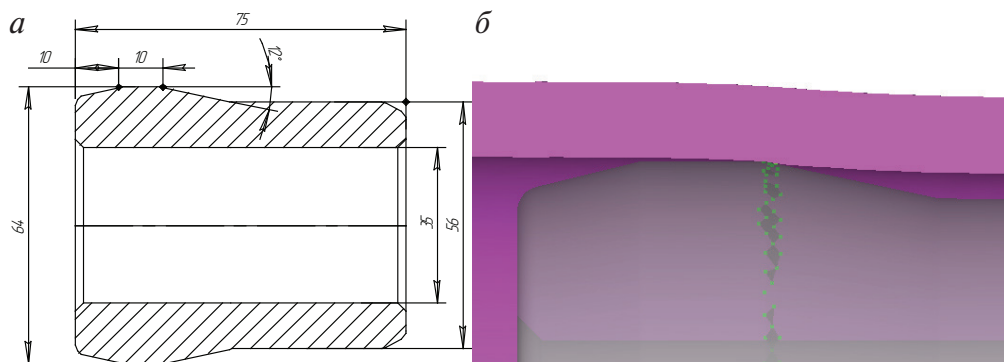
Оправка с коническим участком рабочей поверхности — *а* и длина контакта внутренней поверхности трубы с рабочей частью оправки — *б
